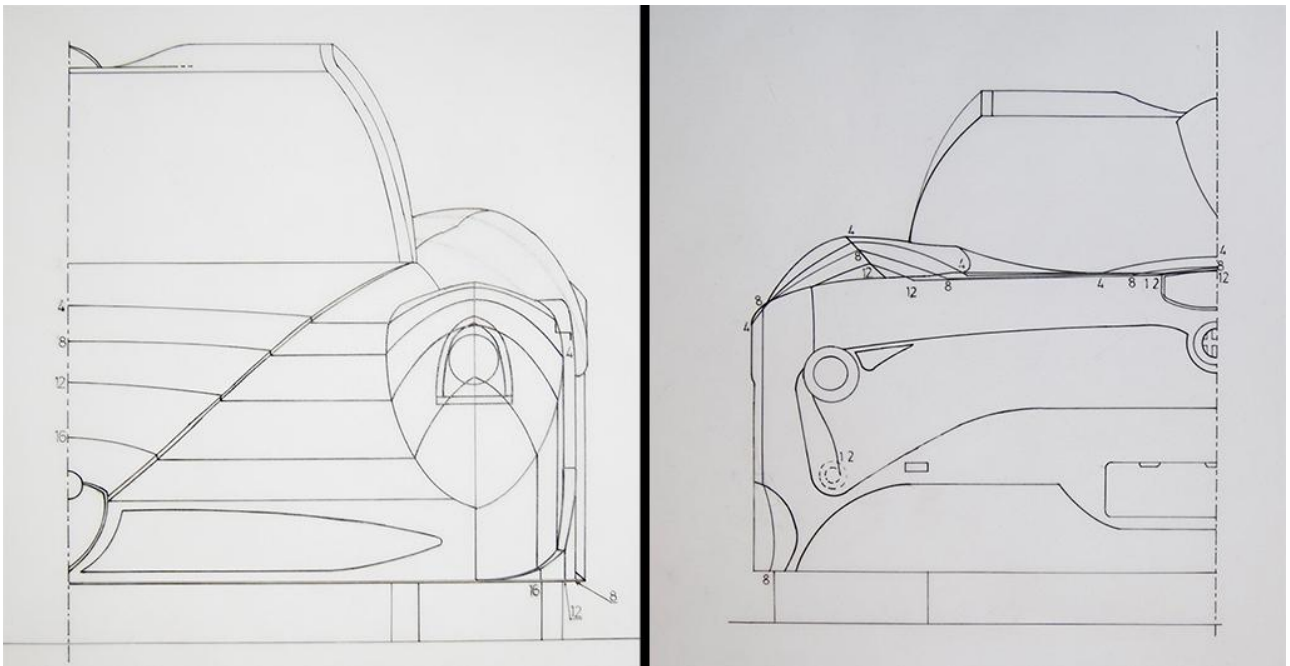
Sezioni trasversali sui prospetti anteriore e posteriore
